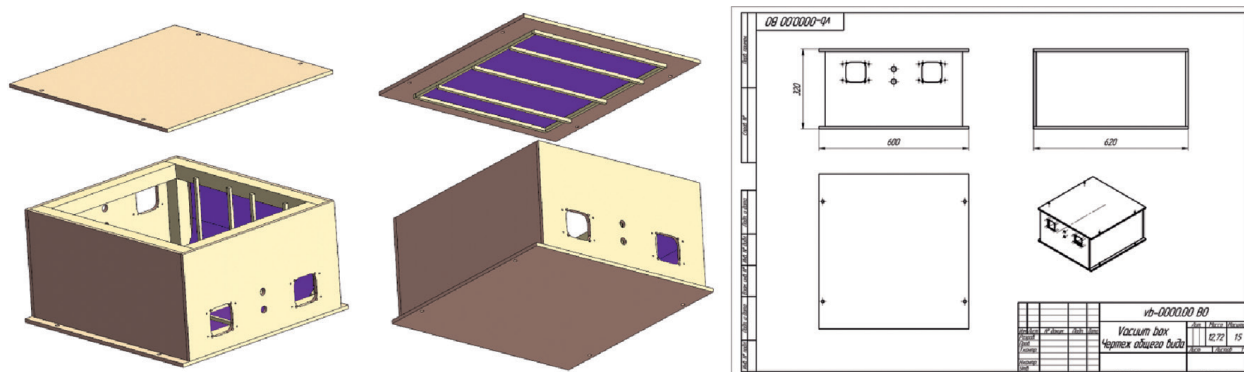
Конструкция корпуса экспериментального образца установки: *а* — 3D-модель; *б* — чертеж общего вида
